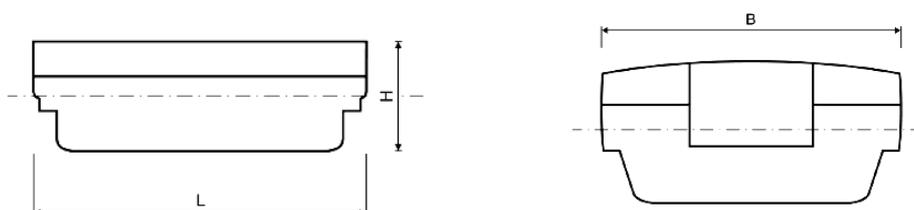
Габаритні розміри перетворювача витрати SHARKY FS 473 фланцеве з'єднання
